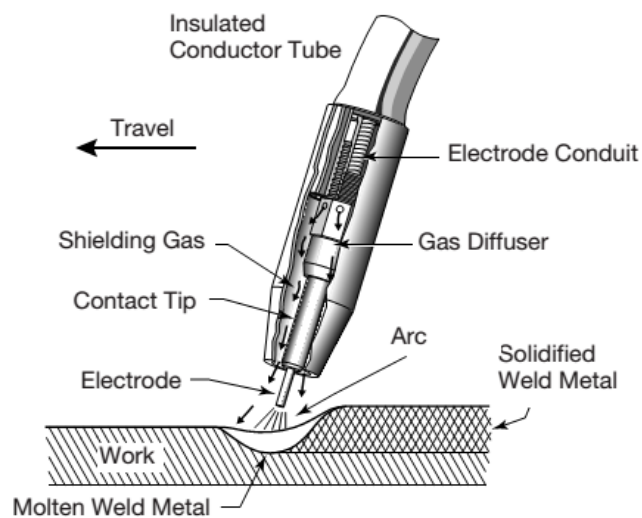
Processo de soldadura MIG/MAG [9]
